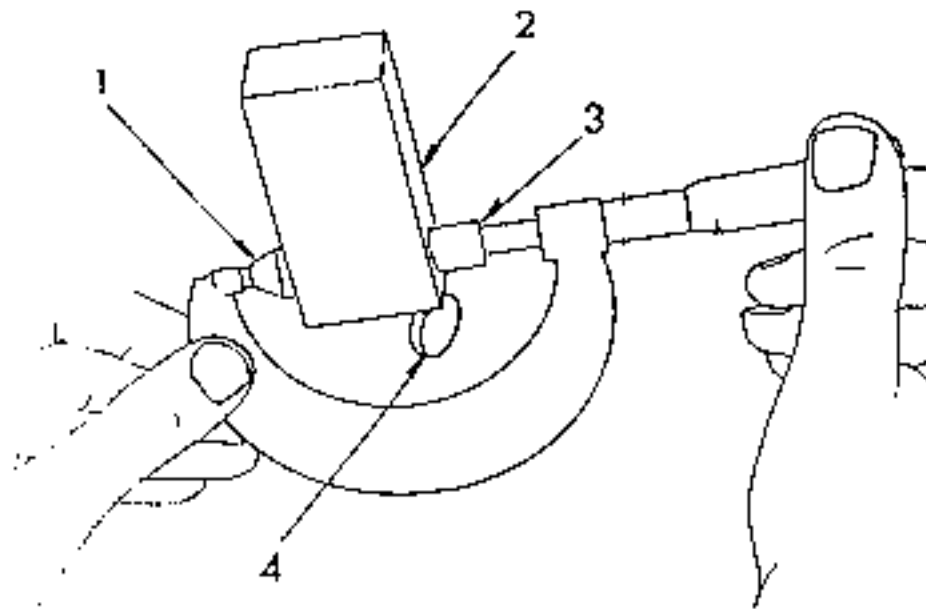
Ausmessen des Messblocks mit einem Mikrometer. Die ausgemessene Länge entspricht der gemessenen Eingriffstiefe.
